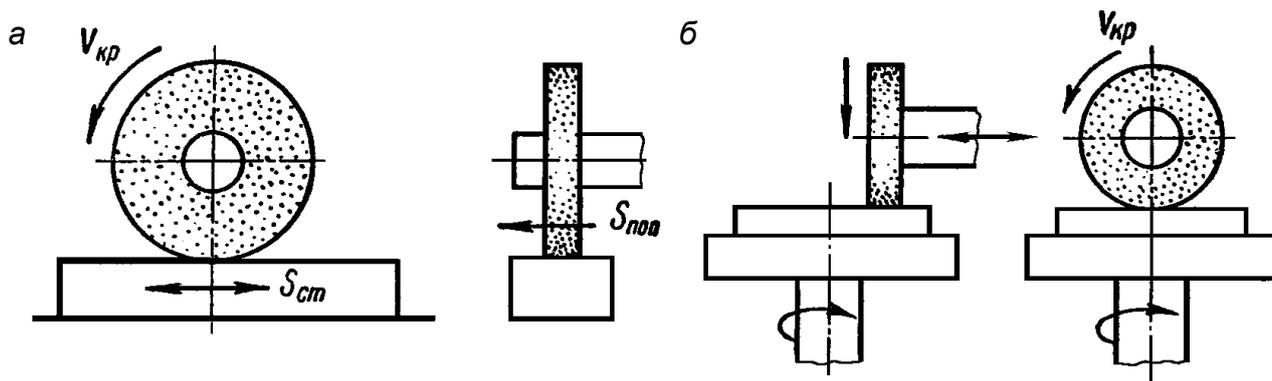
Основные схемы шлифования плоскостей периферией круга: *а* – при возвратно-поступательном движении стола станка с обрабатываемой заготовкой; *б* – при закреплении обрабатываемой заготовки на вращающемся столе
